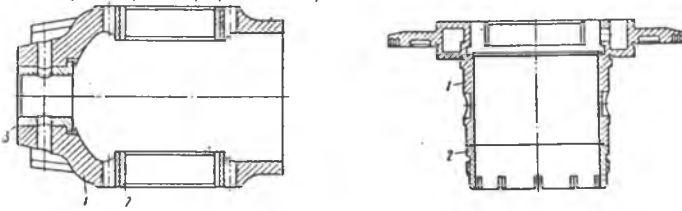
Ремонт корпуса крейцкоффа способом дополнительных ремонтных деталей:
